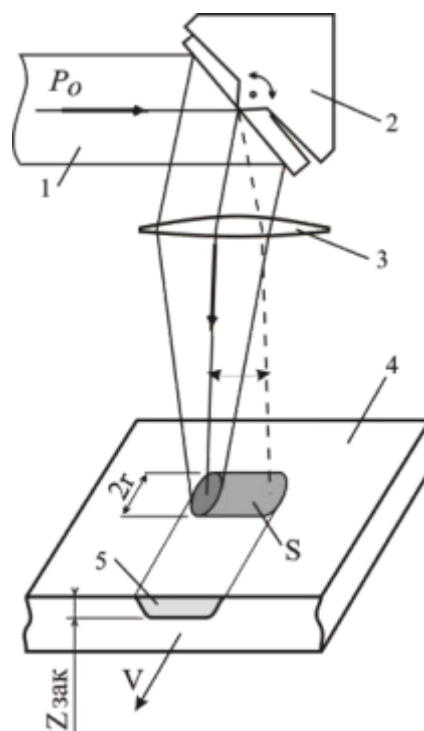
примерная схема лазерной закалки. 1- лазерный пучок; 2 - сканатор с колеблющимся зеркалом; 3 - фокусирующая линза; 4 - обрабатываемый материал. P_0 - мощность лазерного излучения; r - радиус лазерного пучка на поверхности материала; S - площадь зоны нагрева; $Z_{\text{зак}}$ - глубина зоны закалки; V - скорость перемещения обрабатываемого материала относительно зоны нагрева [9].
